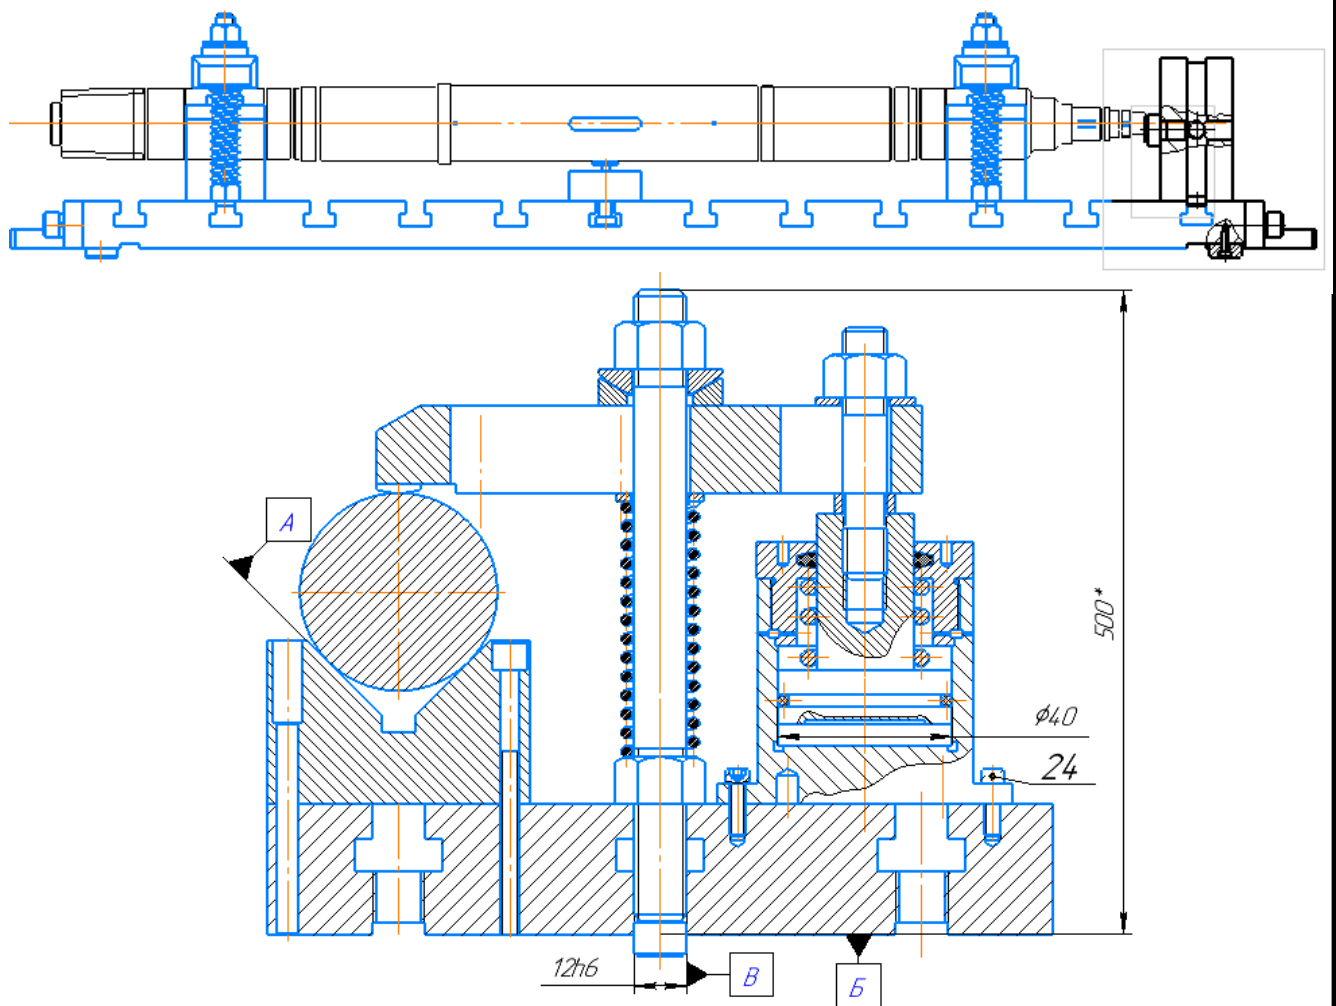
Приспособление для закрепления вала насоса на фрезерной операции
